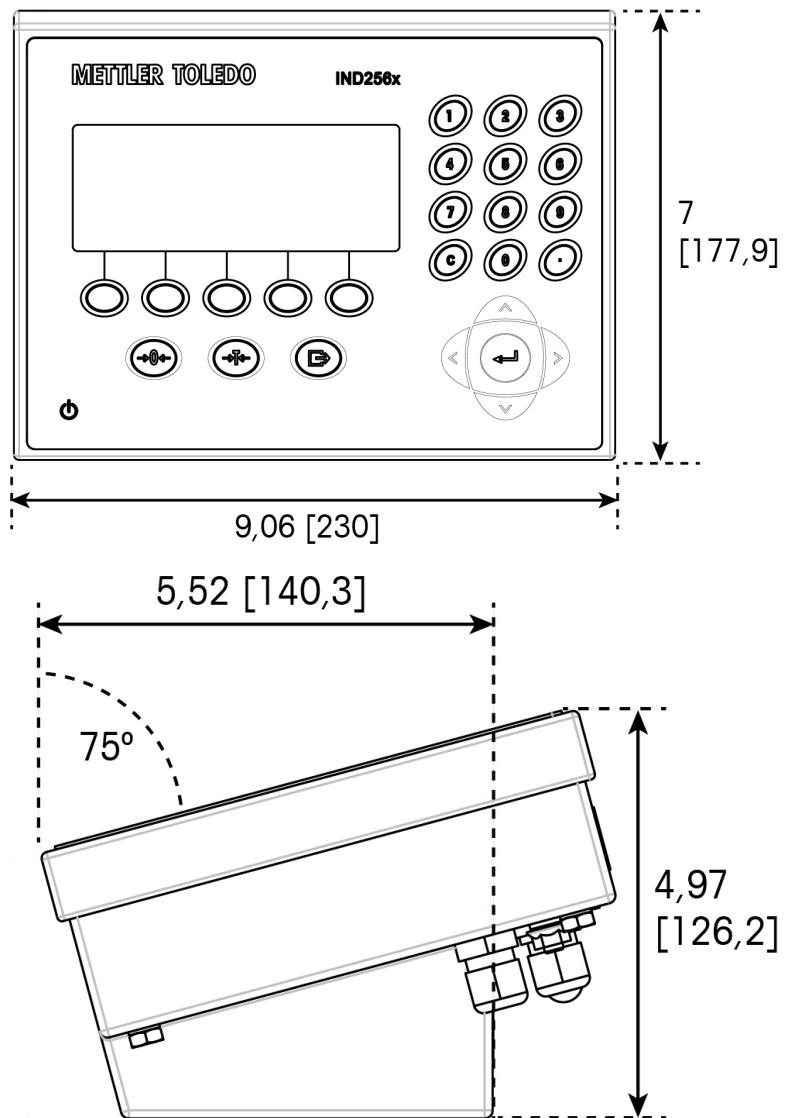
Dimensões do IND256x, Instalação em Bancada
